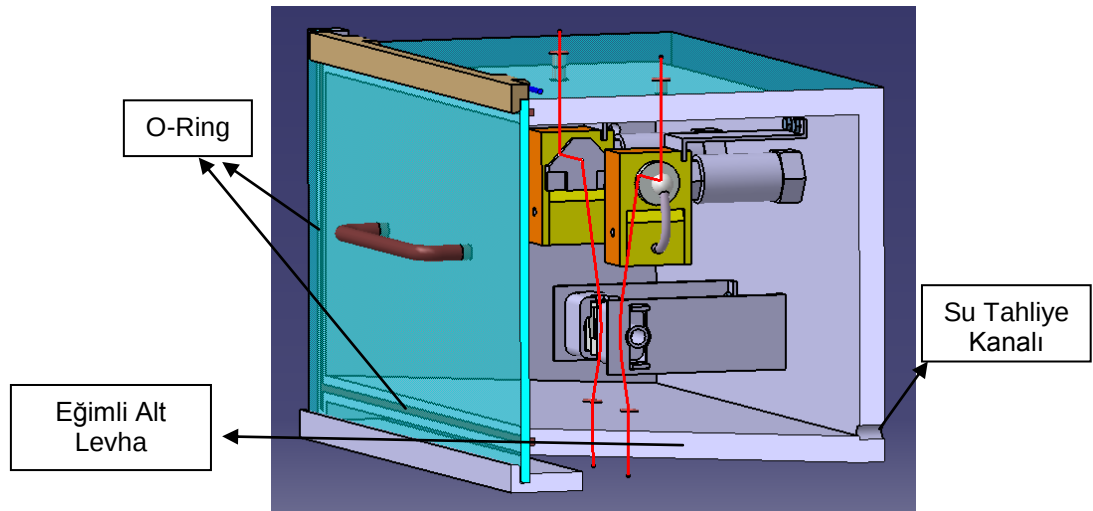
Jet Kutusu Tekstüre Elemanları
